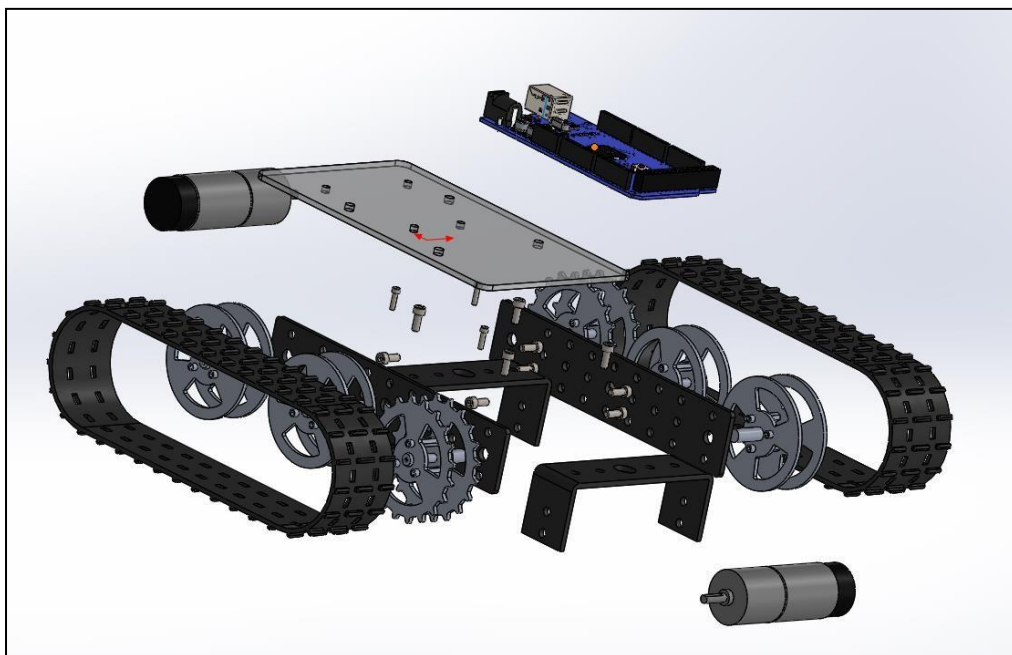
Ensamble Completo CAD (vista Explosionada) – Sensor Car
